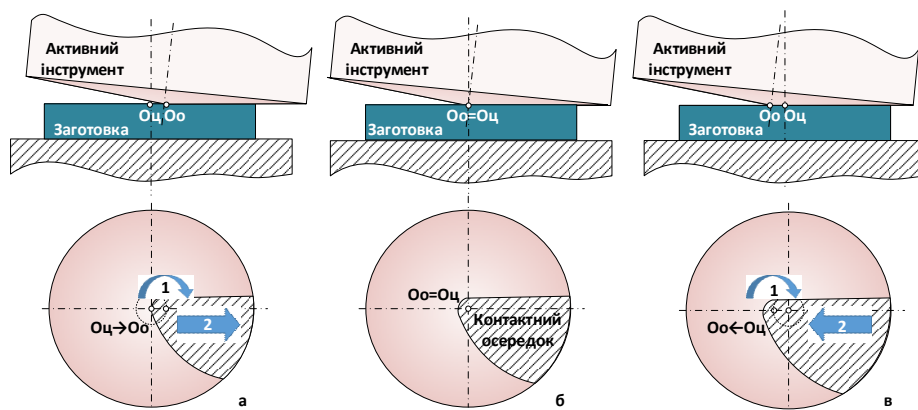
Схеми утворення додаткових сил тертя на контактній поверхні при об'ємному штампуванні обкочуванням (а – центр обкочування O_o зміщений праворуч відносно центру заготовки $O_{\text{ц}}$; б – центр обкочування O_o співпадає з центром заготовки $O_{\text{ц}}$; в – центр обкочування O_o зміщений ліворуч відносно центру заготовки $O_{\text{ц}}$; 1 – напрям кругової траєкторії обкочувального руху контактної осередку; 2 – напрям утворення додаткових сил тертя на поверхні заготовки)
